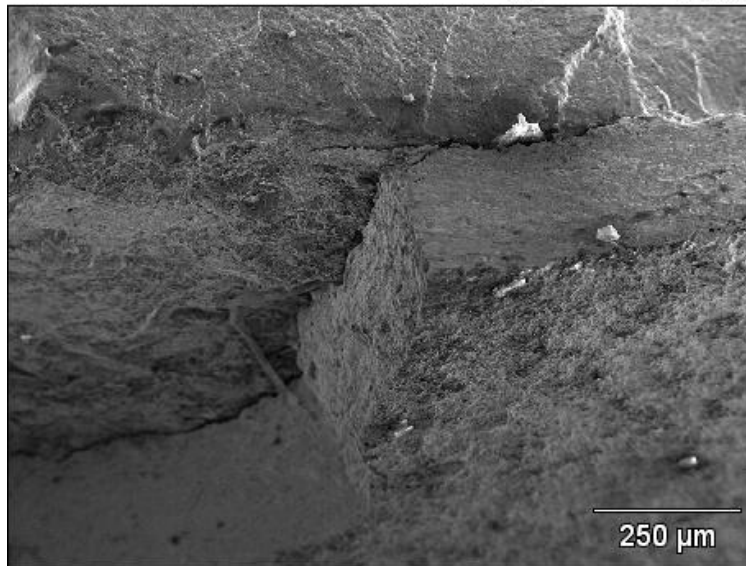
Detalle del conjunto sustrato recubrimiento en la zona de fractura
